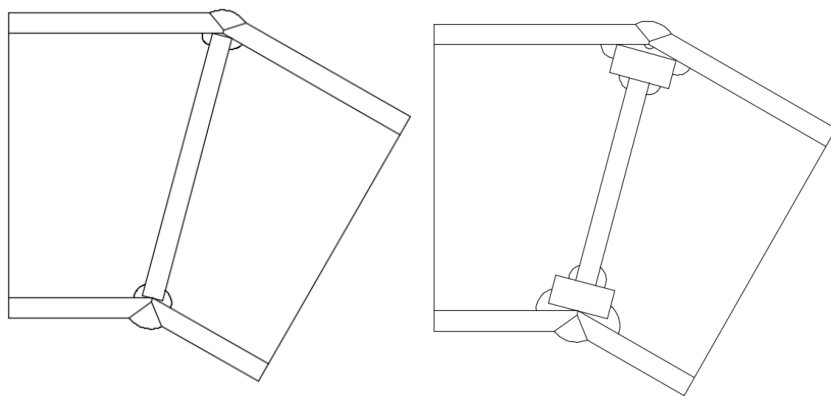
Использование бобышки для разнесения сварных швов
